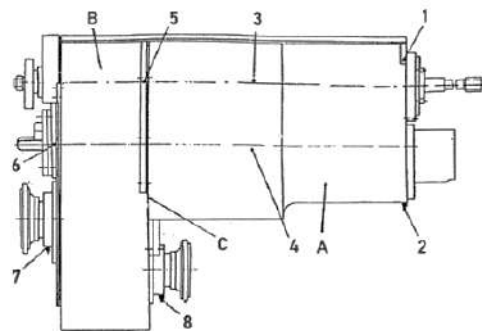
Коробка передач трактора з роздавальною коробкою: 1-8 – точки контролю вібрації; А – коробка передач; В – роздавальна коробка; С – плоскість з'єднання коробки передач і роздавальної коробки
